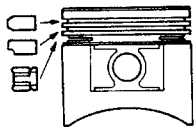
Расположение поршневых колец (См. Раздел 9)
